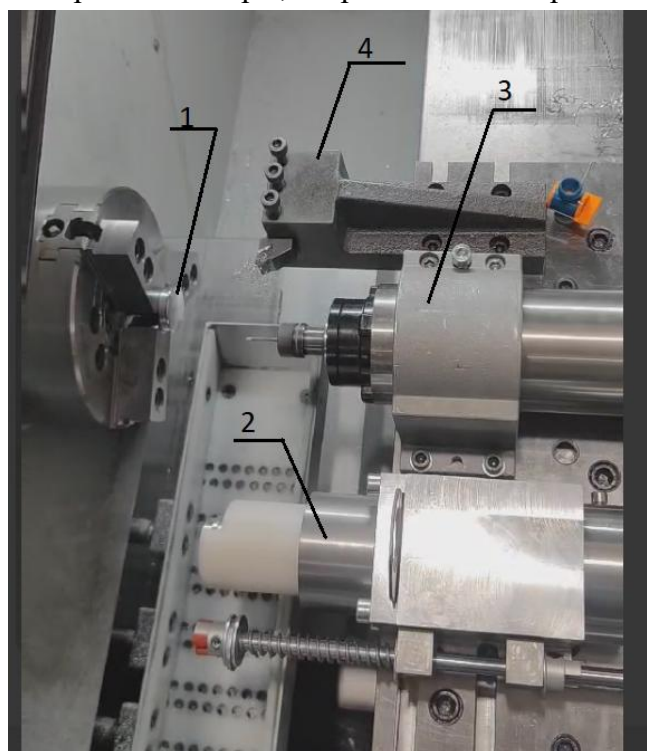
Фото встановленого подавача деталей на супорт верстата (поряд встановлено мотор шпиндель для свердління отворів)
